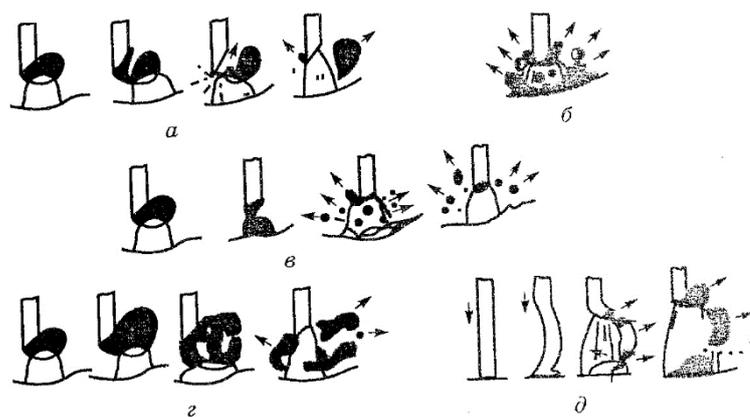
Основные виды разбрызгивания при сварке в CO_2 :
